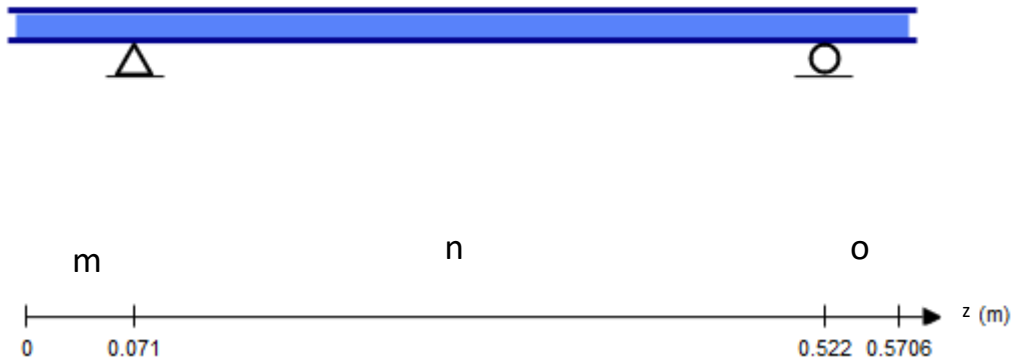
Eje planteado con los apoyos. Fuente propia.
